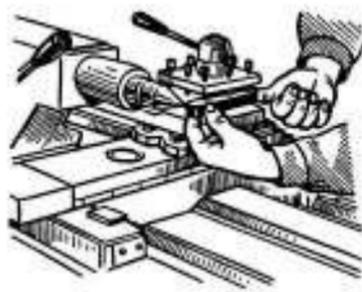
Установка реза в резцедержателе по оси центров станка
